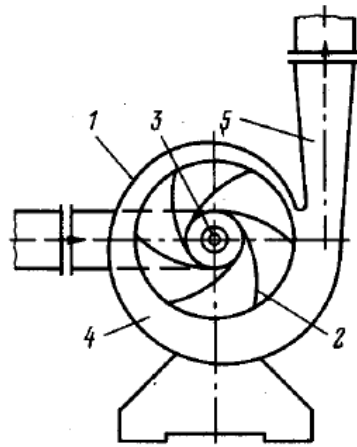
Схема лопатевої турбіни центробіжного типу: 1 – корпус; 2 – лопать; 3 – вхідний отвір; 4 – спіральний відвід; 5 – напірний патрубок
